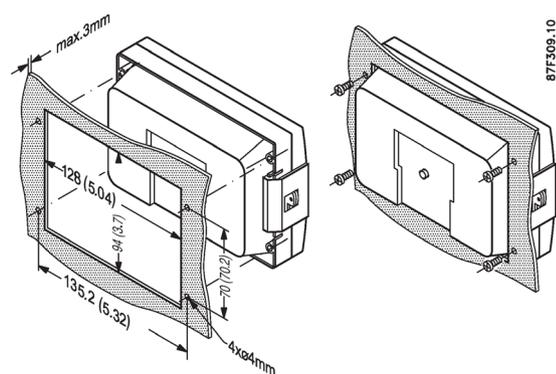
Montaje en panel, dimensiones en mm (pulgadas)
